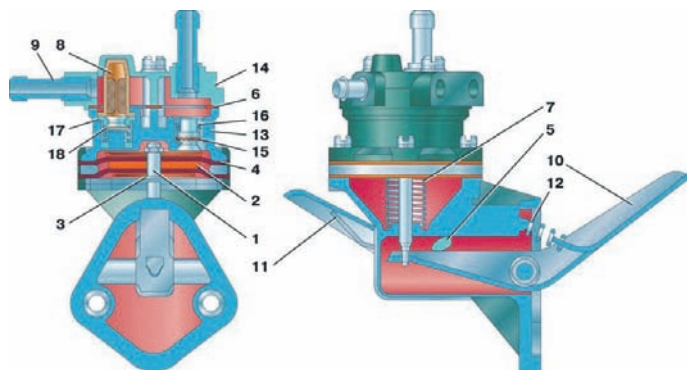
Паливний насос 2105-1106010-50: 1 - корпус; 2 - прокладка дистанційна внутрішня; 3 - шайба ущільнювальна; 4 - діафрагма; 5 - эксцентрик; 6 - прокладка кришки; 7 - пружина центральна; 8 - елемент фільтрувальний; 9 - патрубок;
